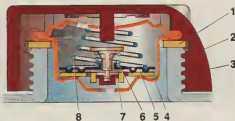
Пробка расширительного бачка автомобиля ВАЗ-2108. 2109: 1 - уплотнительная прокладка; 2 - резиновая прокладка с пазом; 3 - горловина бачка; 4 - латунный блок клапана; 5 - выпускной клапан; 6 - пружина выпускного клапана; 7 - впускной клапан; 8 - пружина впускного клапана.
